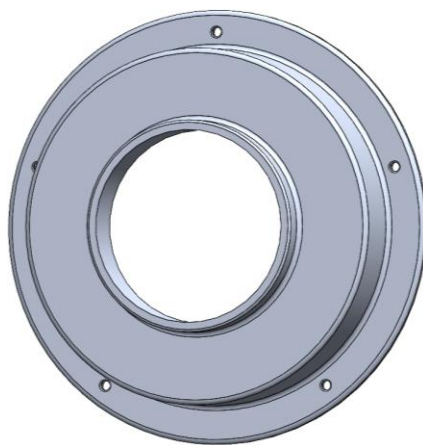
Modelo geométrico CAD 3D de la tapa posterior de la carcasa: vista frontal.
